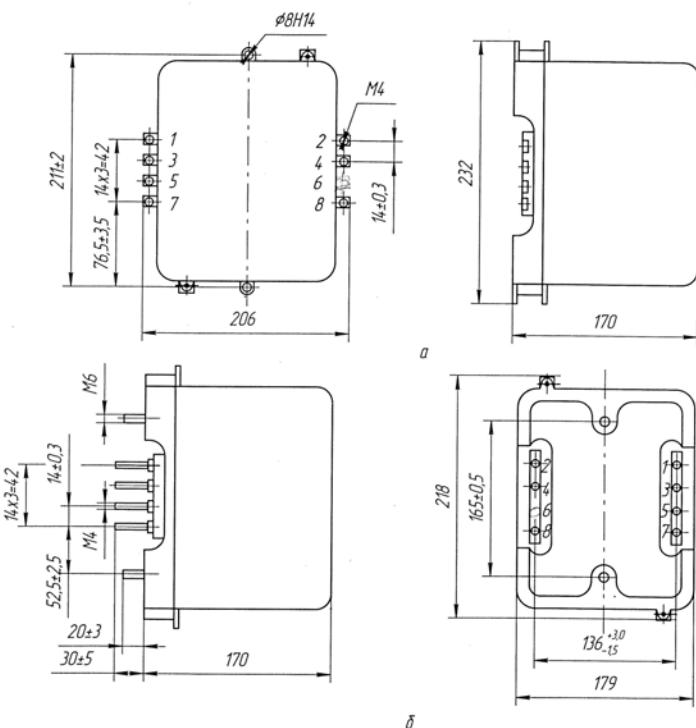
Габаритные, установочные и присоединительные размеры блоков питания типов БН-11, БН-11/2
